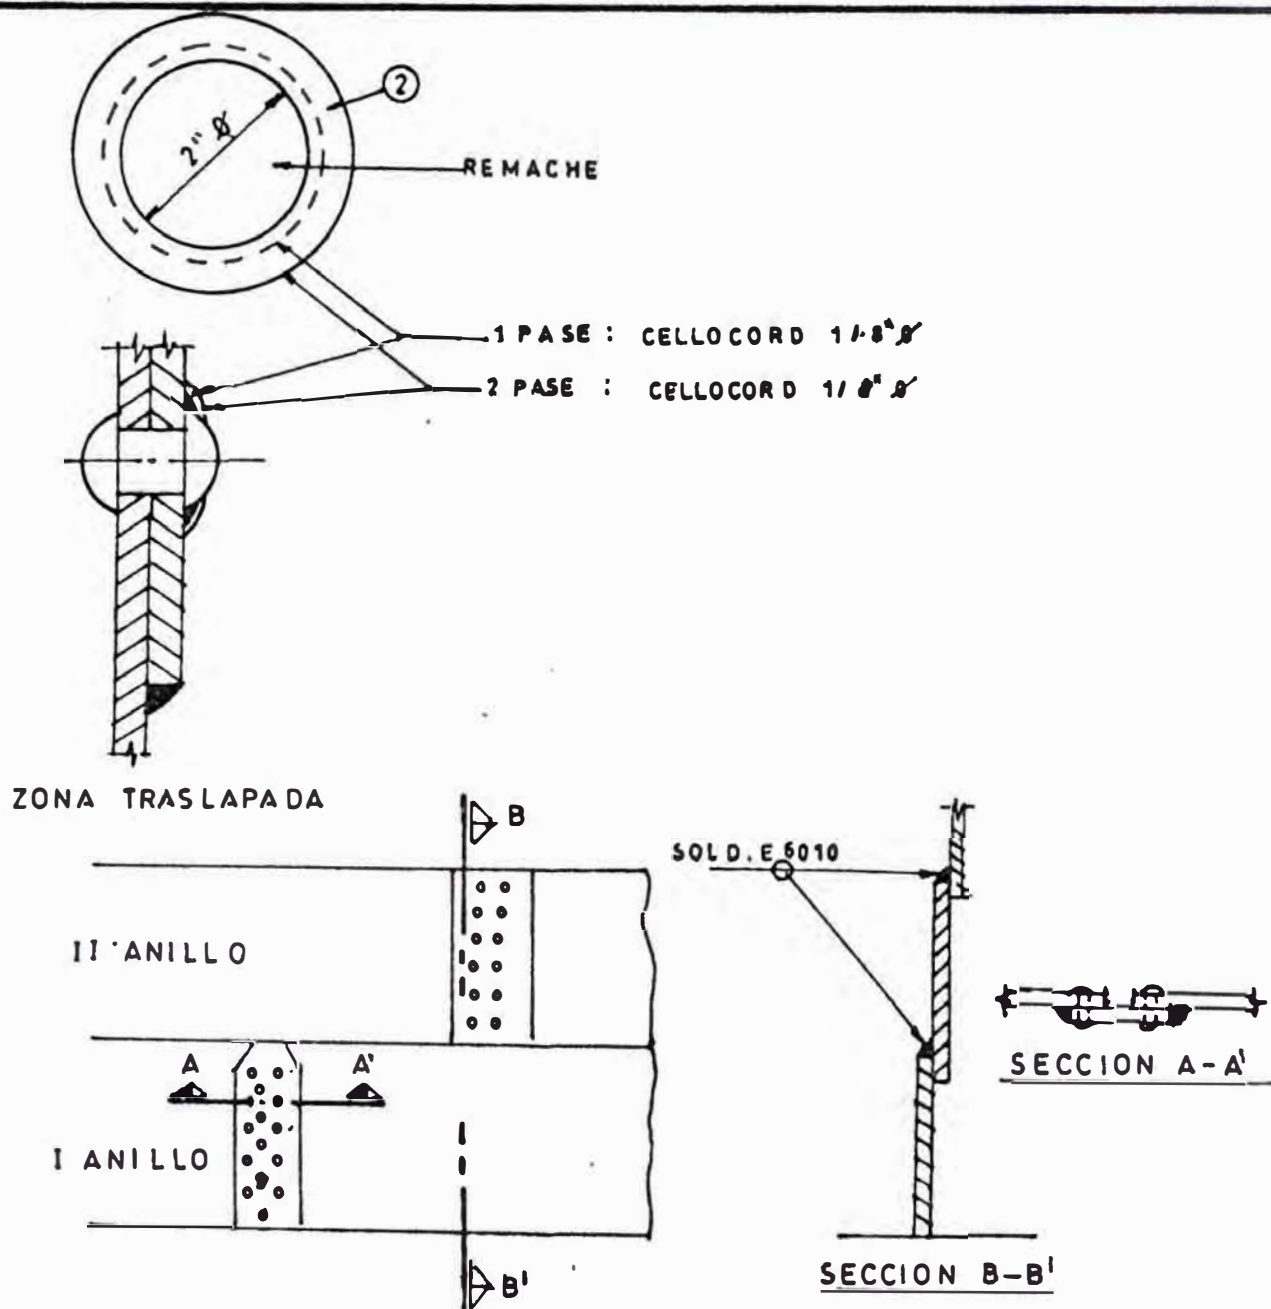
5 SELLADO DE REMACHES Y JUNTAS TRASLAPADAS SOLDADAS
